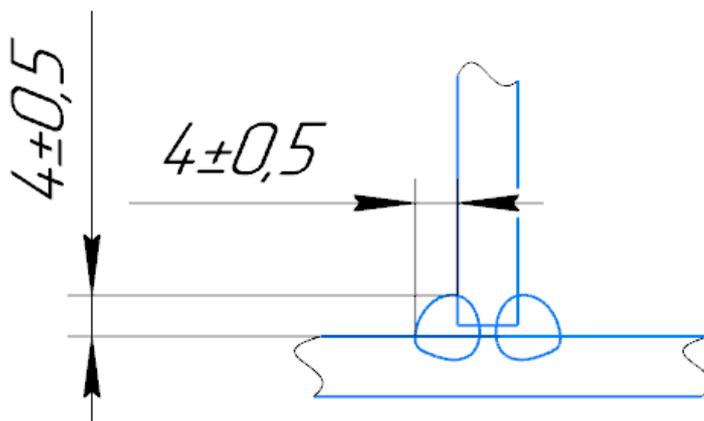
Разделка кромок и размеры сварного шва ТЗ ГОСТ 14771-76
